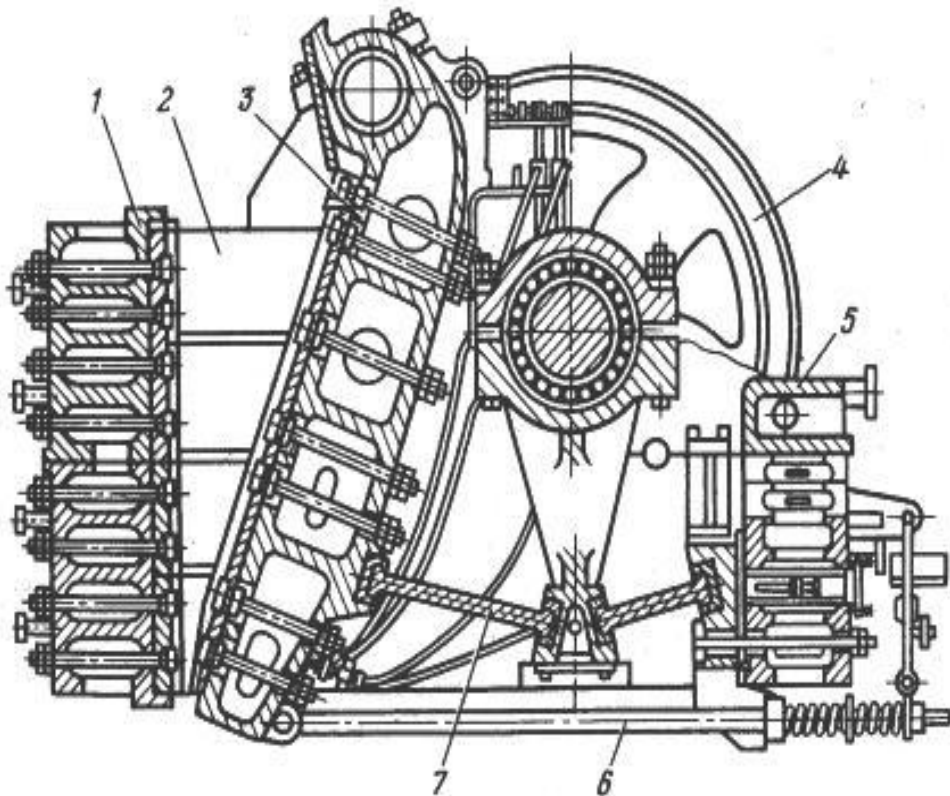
Дробарка СМД-111: 1 – нерухома щока; 2 – бокова футеровка; 3 – рухома щока; 4 – маховик; 5 – задня стінка; 6 – тяга; 7 – розпірна плита
